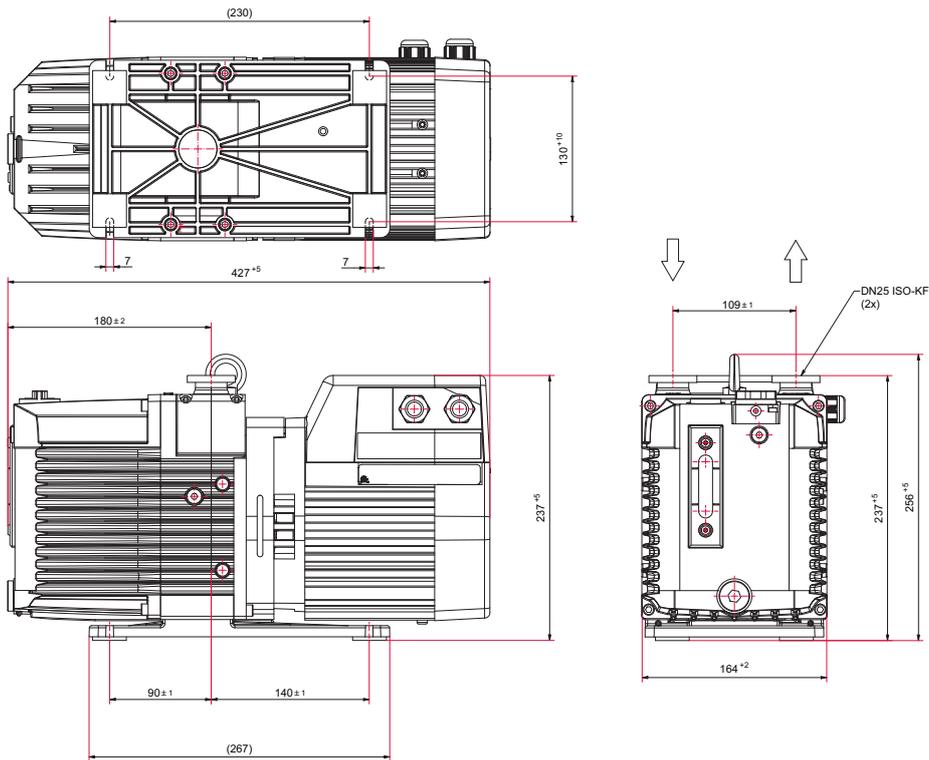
Abmessungen DuoVane 12 mit Dreiphasenmotor
